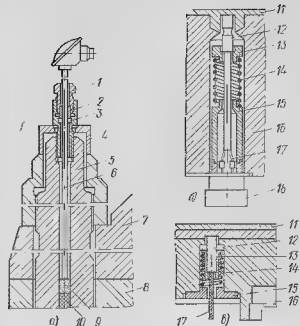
Контроль температуры металла ЦВД (а); установка палитровых термометров сопротивления ТСП-364 во выходящих опорного подшипника (б) и опорного подшипника (в).
